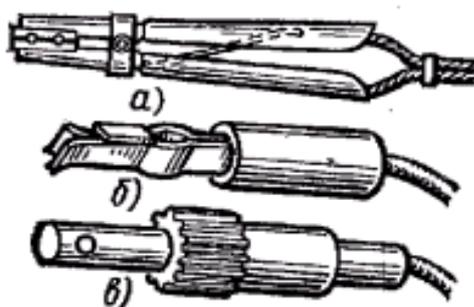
Электродержатели для ручной дуговой сварки (а – пружинный, б – пластинчатый, в – винтовой).
